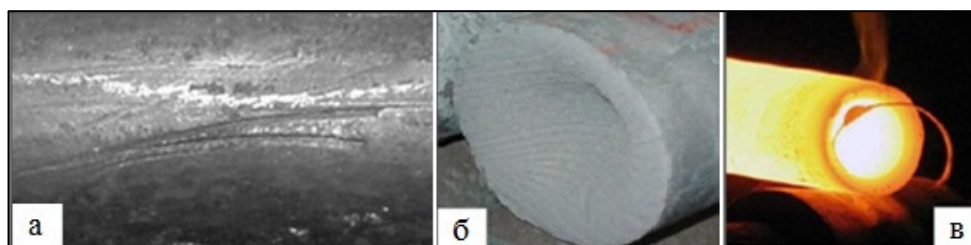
Вмятина на поверхности готовой трубы (а), образование утяжины на заготовке (б) и полукольца на гильзе (в)
